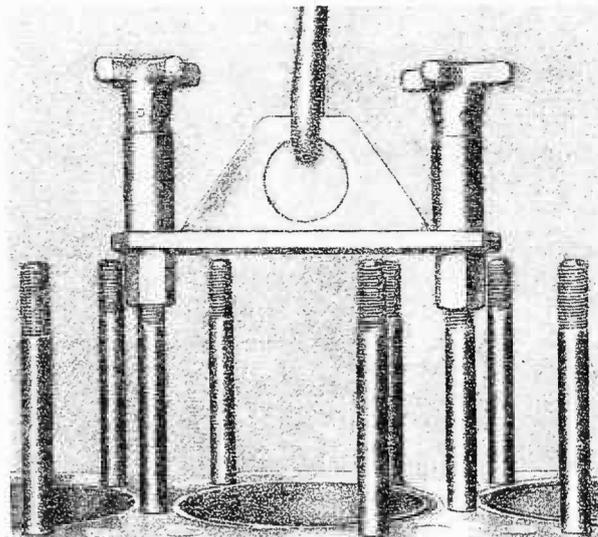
Abheben des Zylinderblockes mit Hebezeug
